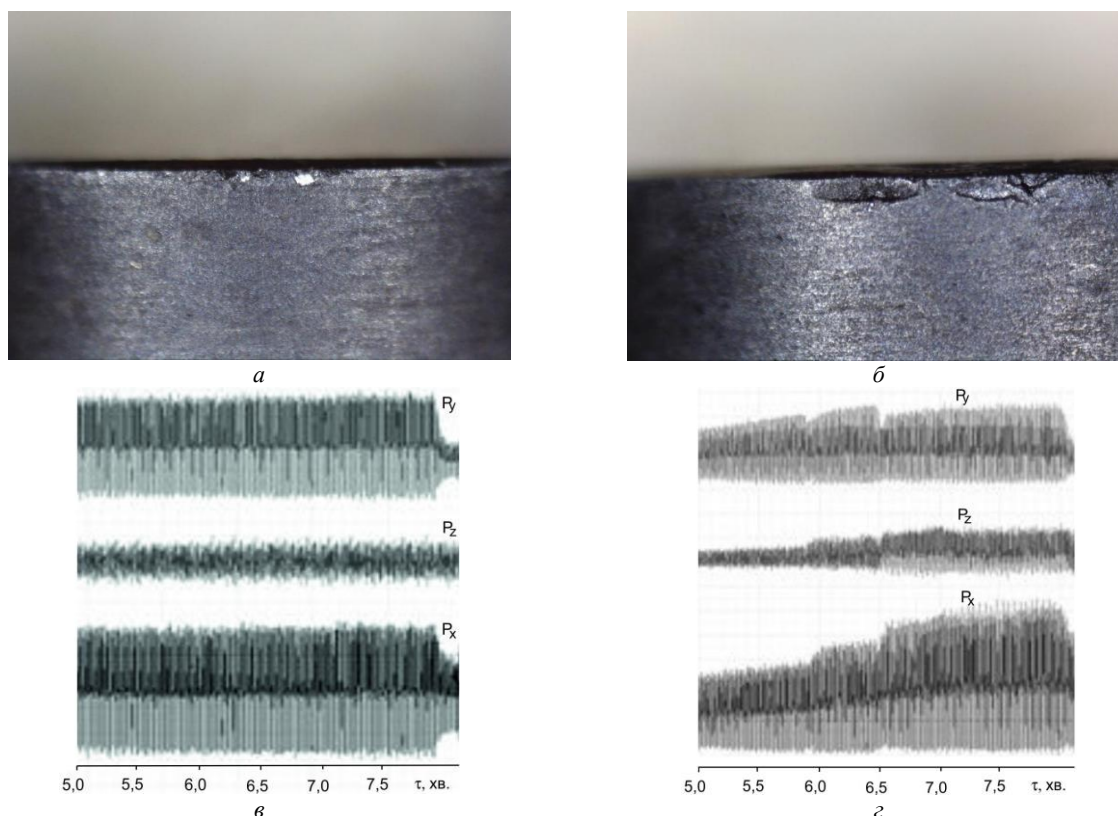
Контактні ділянки (а, б), загальний вигляд сигналів складових сили різання (в, з): інструмент, оснащений PcBN (5% Ti) (а, в), оснащений PcBN BL (б, з), ($v = 220$ м/хв., $t = 0,2$ мм, $S = 0,38$ мм/об)
